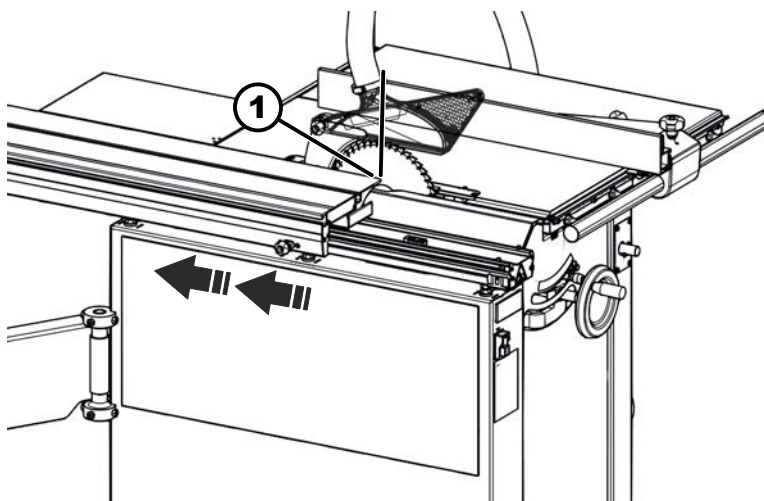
Ajustar la jaula de rodamiento del carro deslizante
